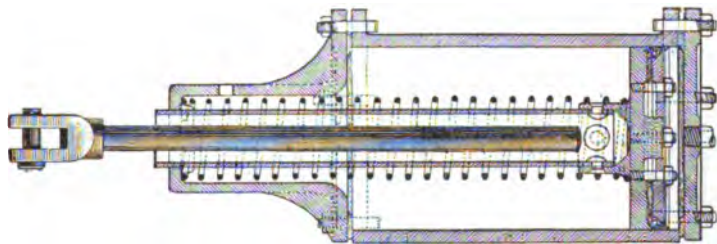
Coupe d'un cylindre à freins de la Standard Air-Brake Co.
